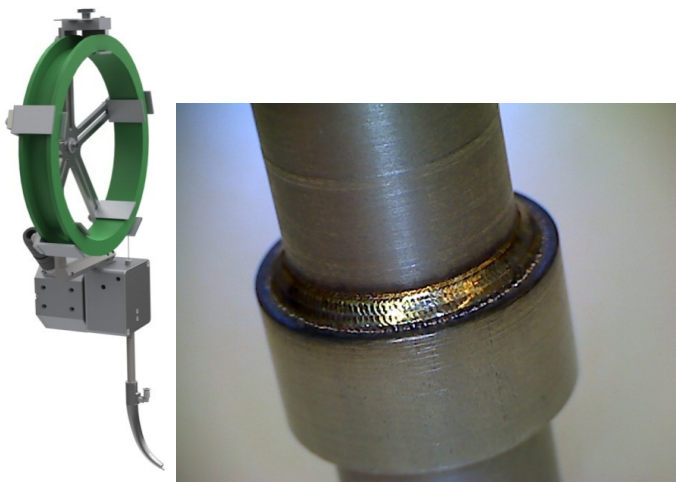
Gesamtaufbau für die Drahtzufuhr bei Auftragschweißprozessen
